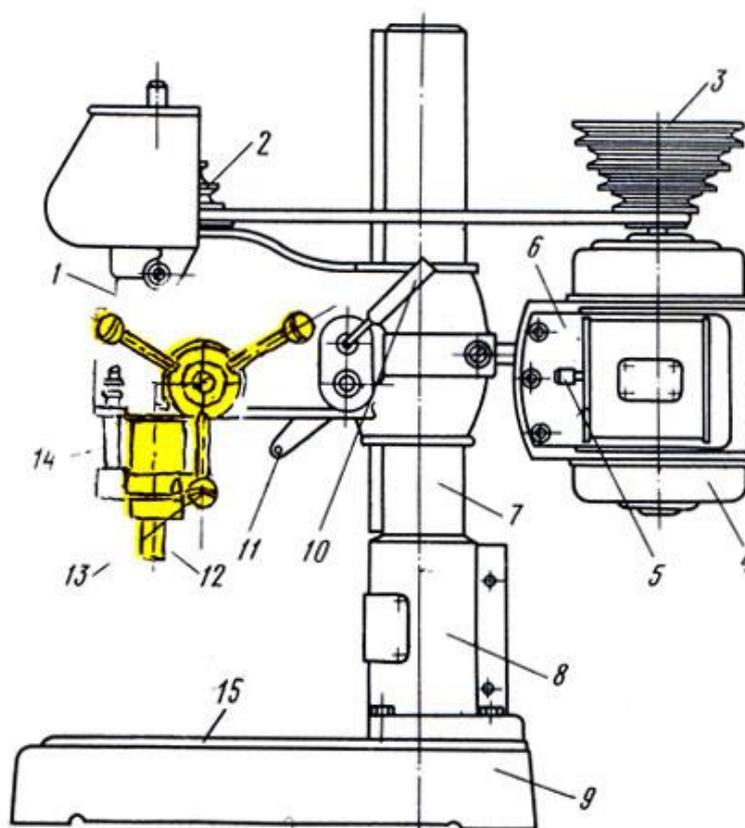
Настольно-сверлильный станок НС-12А: 1 - шпиндельная бабка, 2 - шкив шпинделя, 3 - ступенчатый шкив, 4 - электродвигатель, 5 - вилка, 6 - плита двигателя, 7 - колонна, 8 - кронштейн, 9 - плита, 10, 11, 13 - рукоятки, 12 - шпиндель, 14 - упор с нониусом, 15 - рабочий стол
